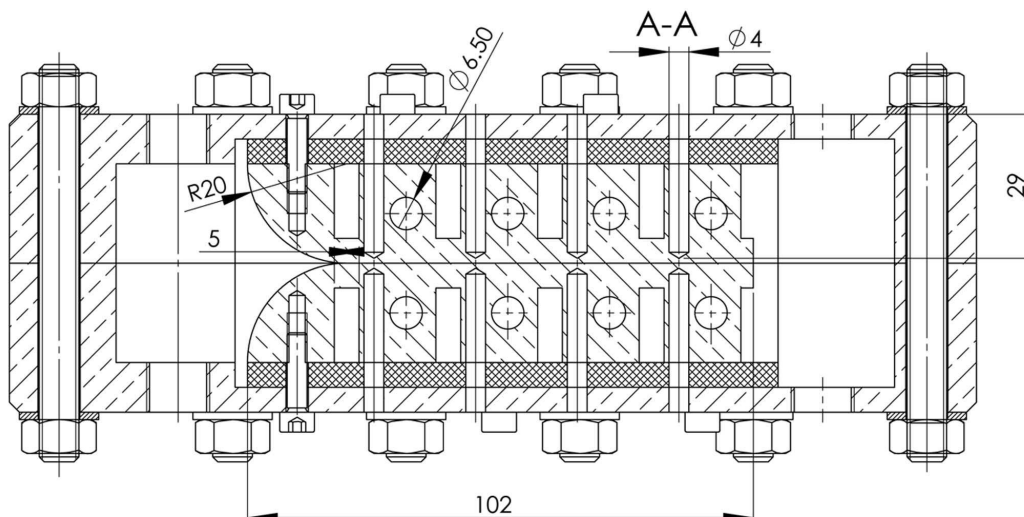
Coupe longitudinale de la section d'essais
